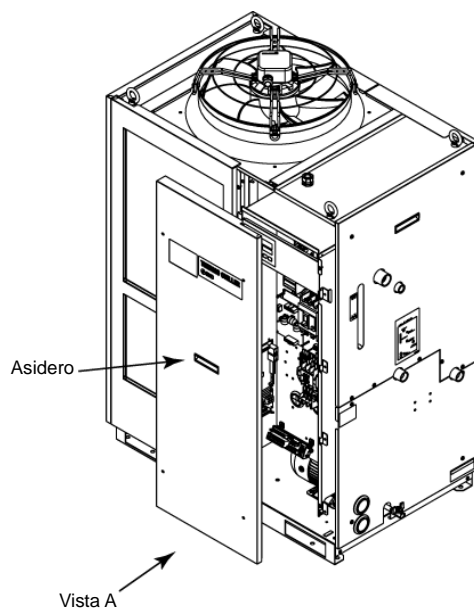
Retire el parte frontal de la unidad eléctrica
